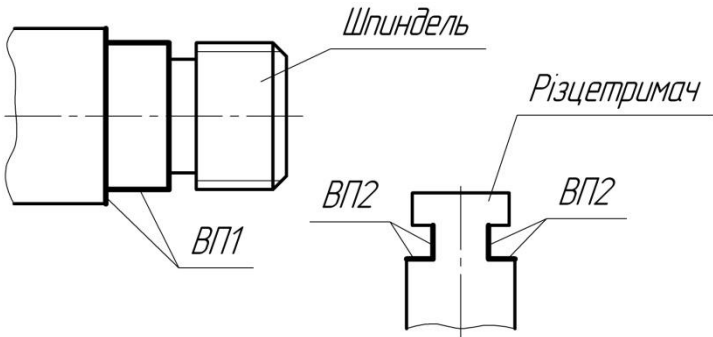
Виконавчі поверхні при обробці валика в патроні
